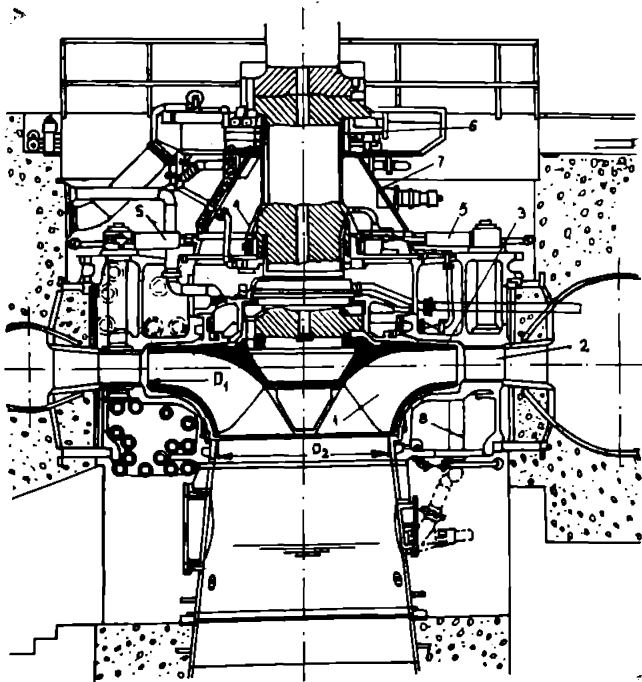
Mașina hidraulică radial-axială reversibilă de la CHEAP Rodund II.
